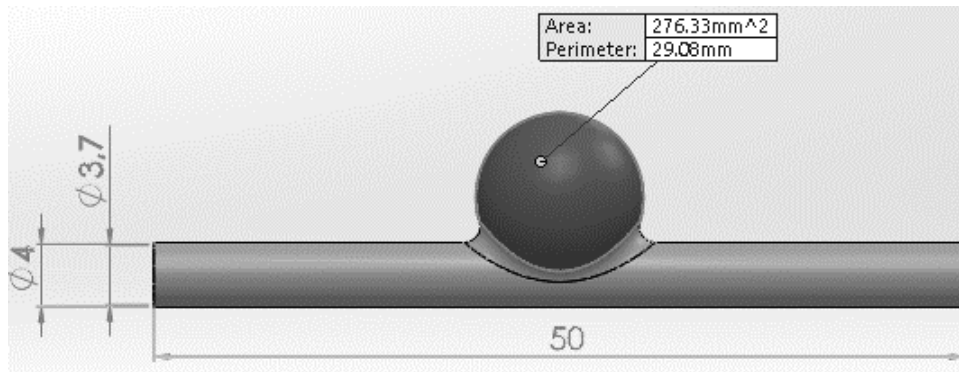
Dimensões e geometria da parede do canal usada para o estudo estrutural (parte exterior).
